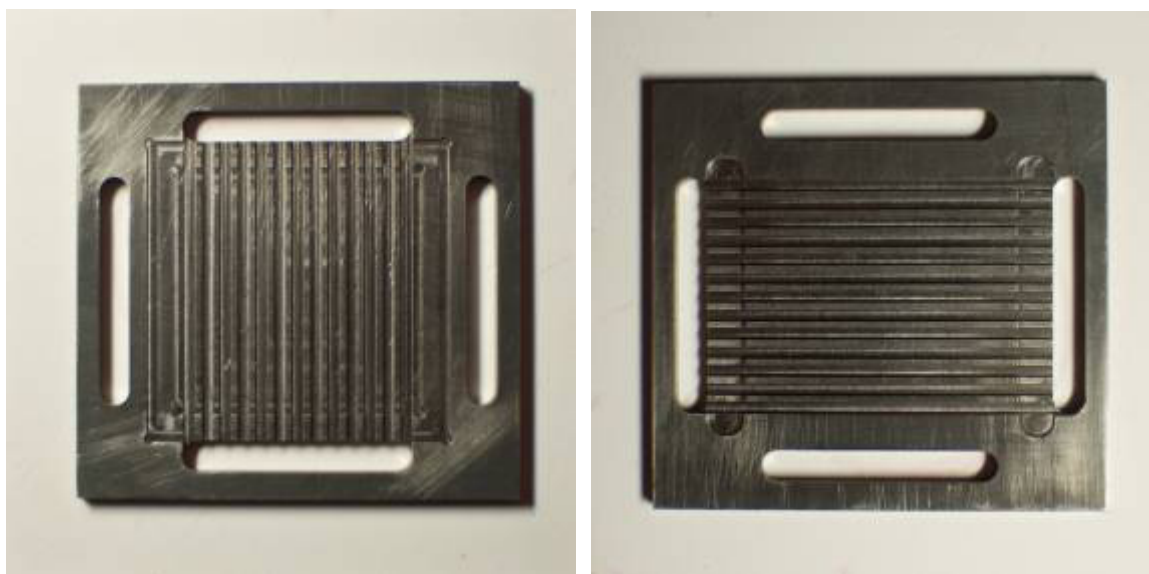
Биполярные токовые коллекторы, изготовленные методом трехмерного фрезерования
